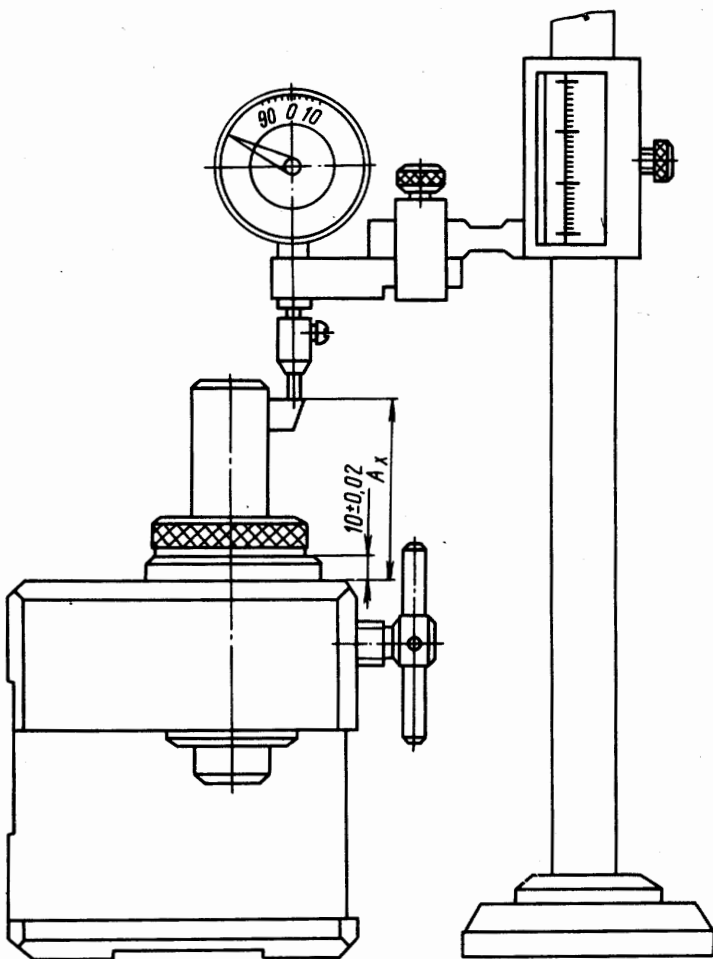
Схема наладки инструмента вне станка. Установка осевого размера
